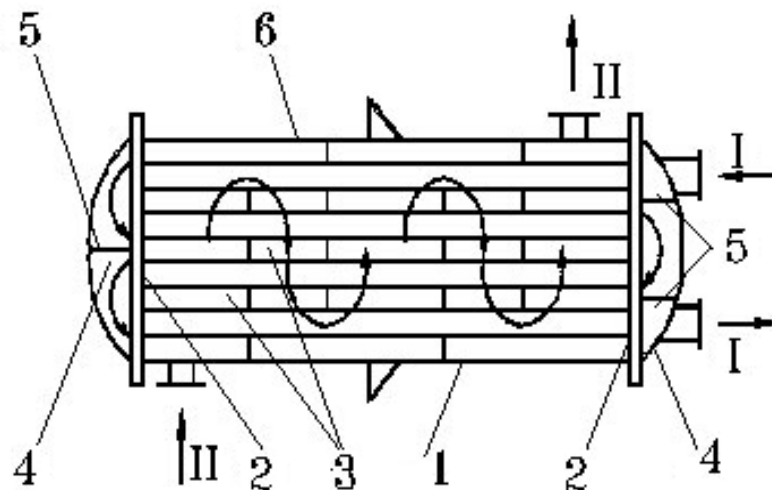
Кожухотрубчастий багатходовий теплообмінники 1 - корпус ; 2 - трубні решітки; 3 - труби; 4 - кришки; 5 - перегородки в кришках; 6 - перегородки в міжтрубному просторі
